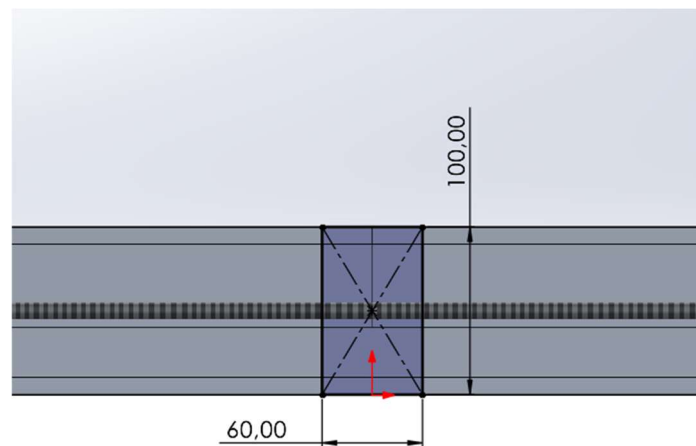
Dimensiones generales de los perfiles de la zona inferior del conjunto.
